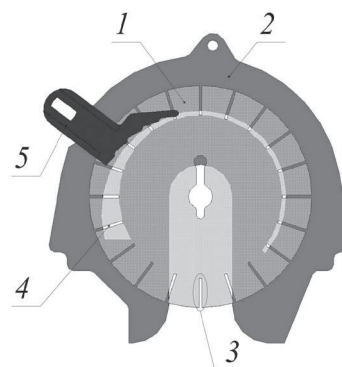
Предлагаемый высевочный диск и прокладка вакуумной камеры
